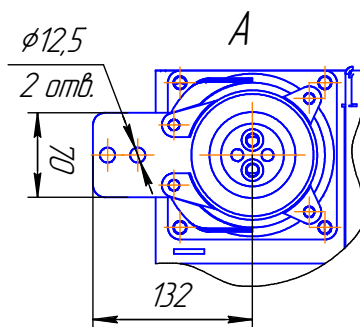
Габаритные, присоединительные и установочные размеры выключателя типа ВВУ-СЭЩ-П6-10-20/1000 КСО-298
